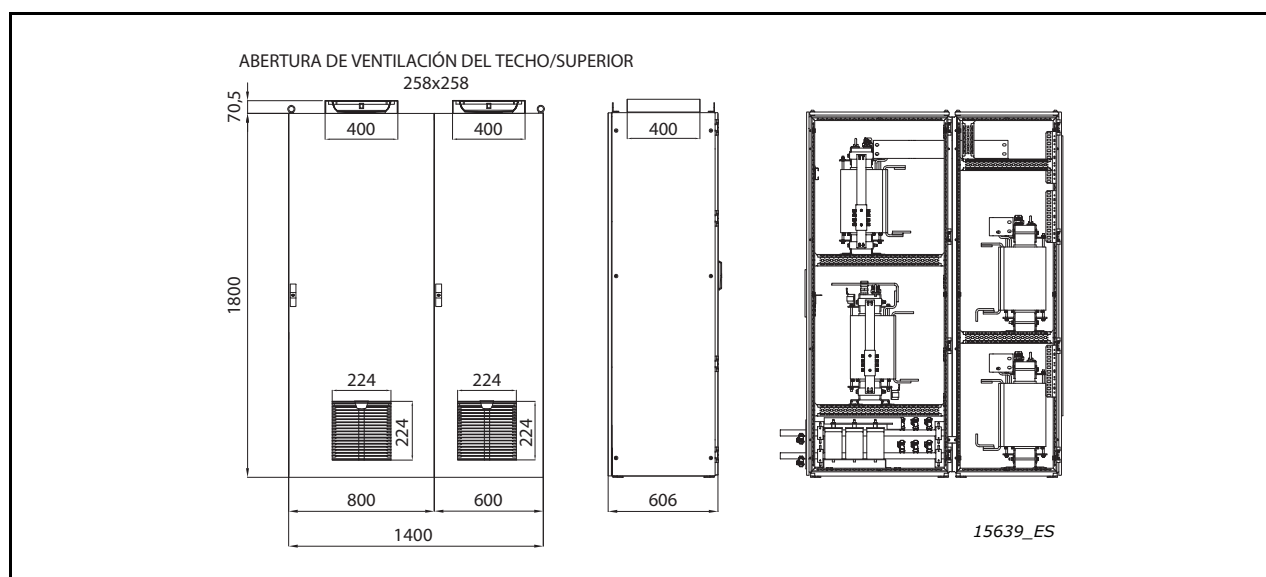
Disposición del RLC 1180/1640/2300 A instalado en una protección
